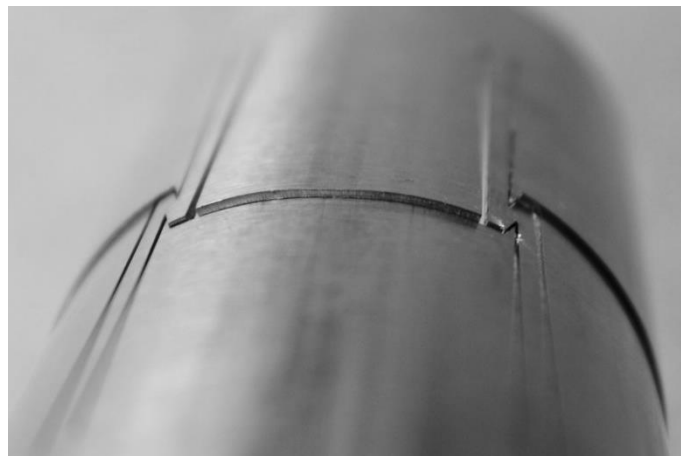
Disallineamento tra le superfici del dispositivo Cantilever Beam.
